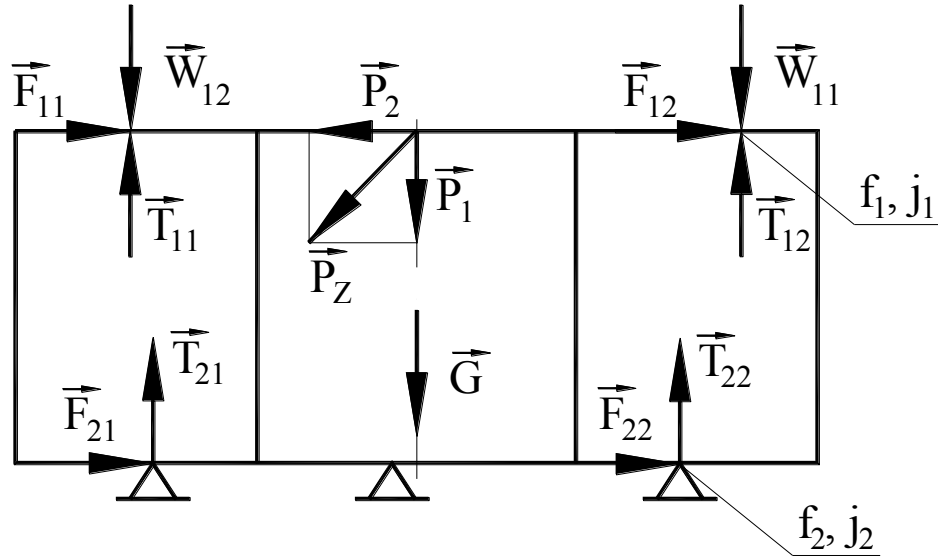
Схема сил, що діють на деталь під час фрезерування площини
